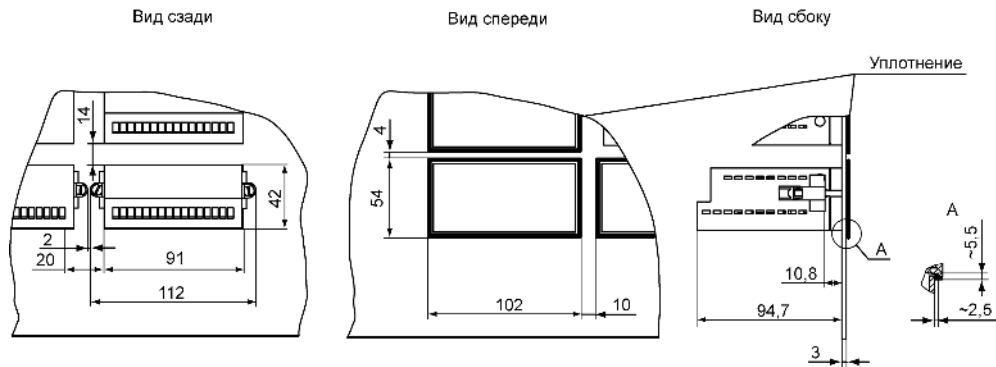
Прибор в корпусе Щ2, установленный в щит толщиной 3 мм
